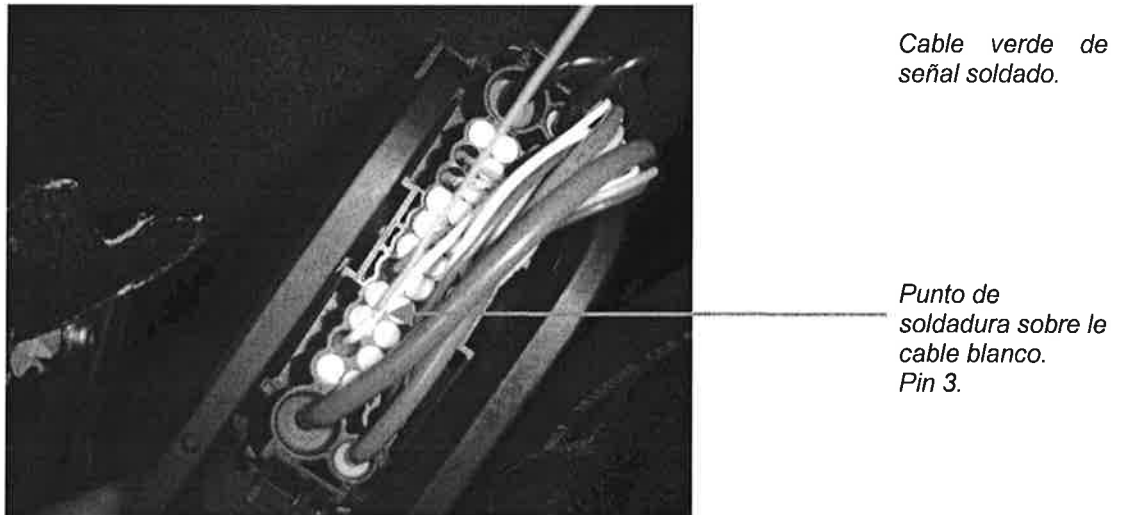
Vista del acceso de cables al conector (parte posterior). El cable verde de señal irá soldado en esta parte, en el pin 3.
